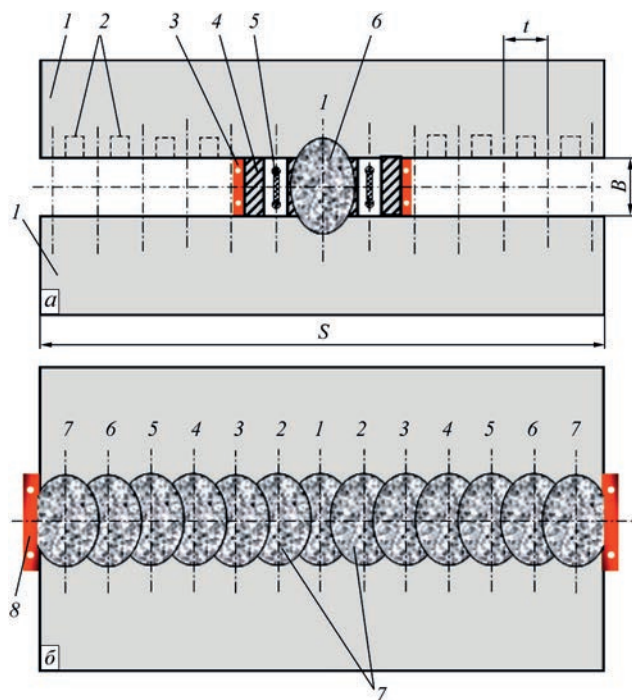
Схема розмітки стику, заварки центральної комірки (а) і виконання суміжних проходів БЕШЗ ПМ (б): 1 – зварювані частини дефектної деталі; 2 – місця установки формуючих вставок; 3, 8 – водоохолоджувальний пристрій; 4 – вставка; 5 – плавкий мундштук; 6 – центральний шов; 7 – суміжні шви; S – товщина деталі (довжина наскрізної тріщини); B – проміжок; t – крок комірок
